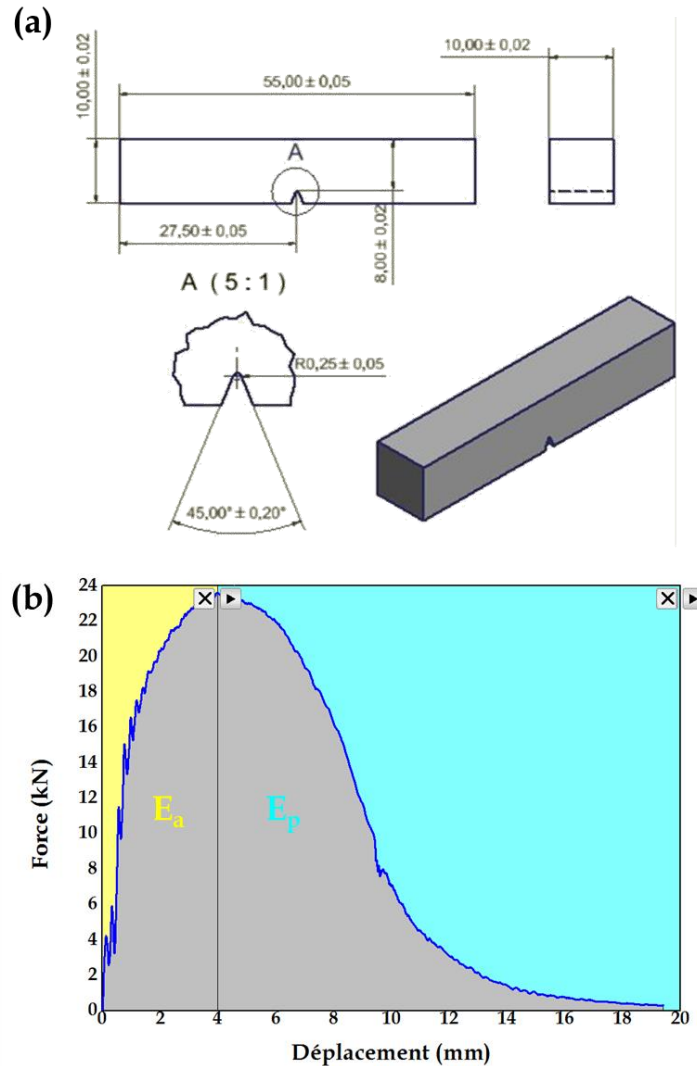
(a) Dessin technique de l'éprouvette entaillée Charpy ;
